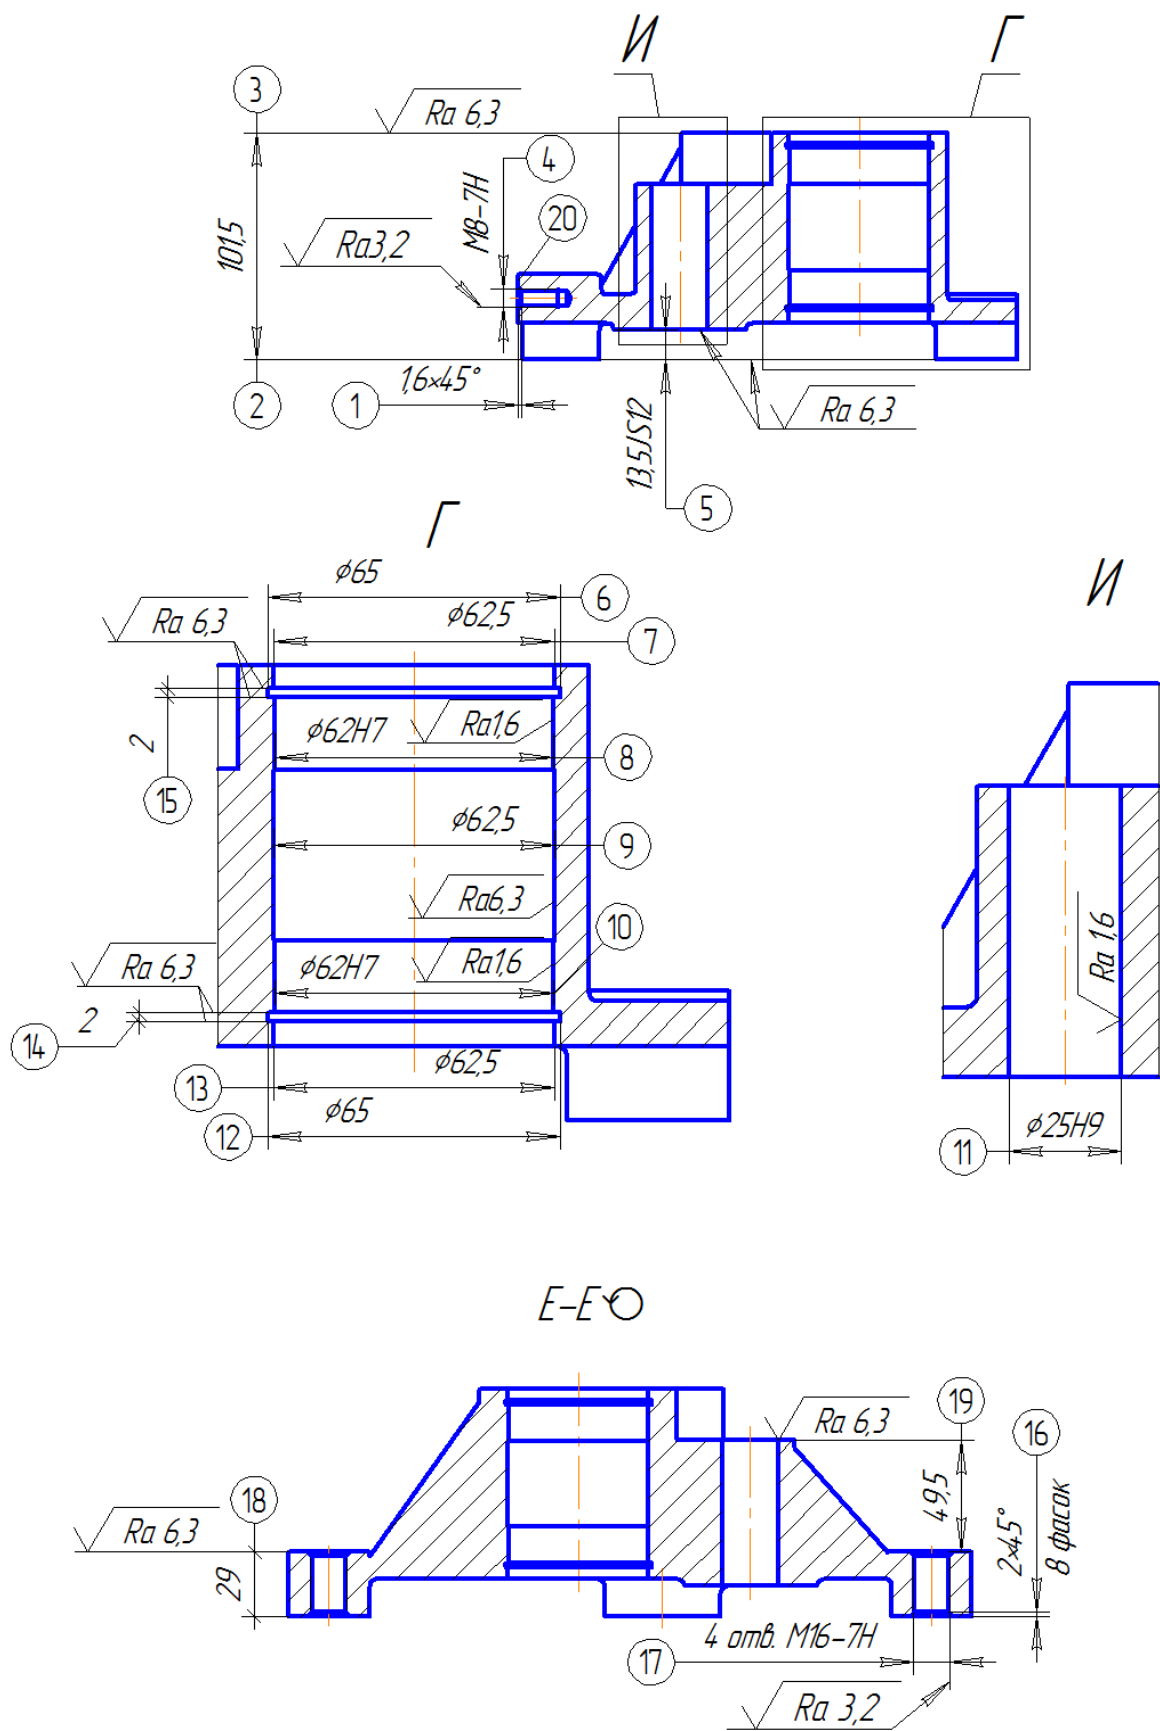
Эскиз детали «Корпус подшипника тягового механизма»
